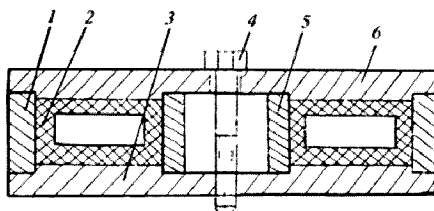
Установка резиновой камеры в металлическую форму для вулканизации:
